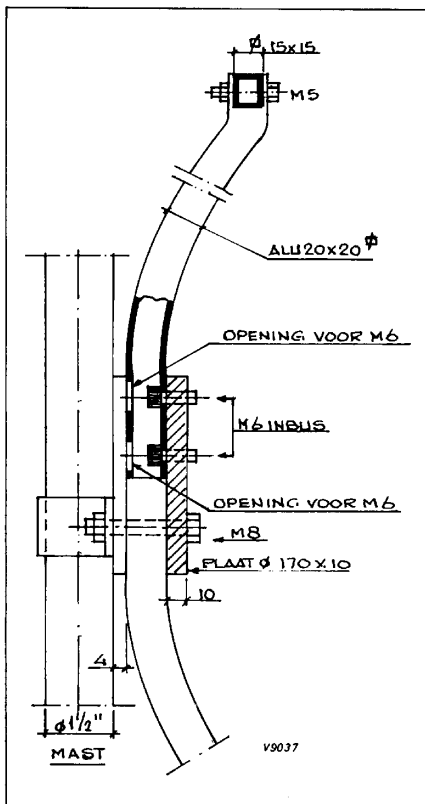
Detail van de bevestiging van de parabool. De constructie is gemaakt van vierkante aluminium pijp. Het geheel is gemonteerd op een ronde aluminium plaat van 10 mm dik.
